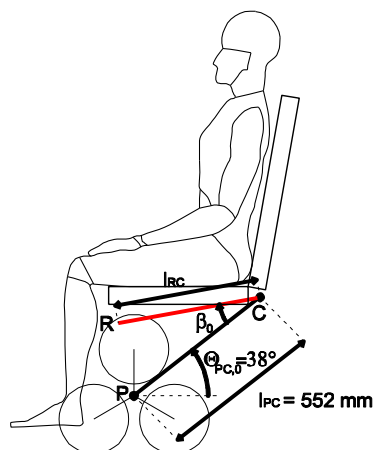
Configurazione e dimensioni scelti per il sotto-telaio PC della carrozzina
